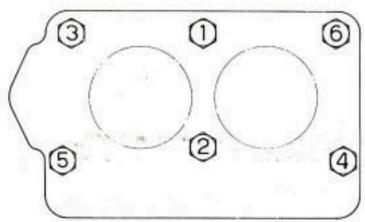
Rimontaggio del motore: schema de l'ordine di serraggio delle viti di fissaggio te;ta cilindri.
